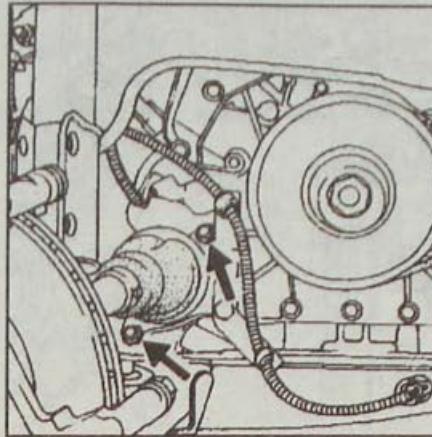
Расположение болтов крепления промежуточной опоры приводного вала в опорном подшипнике
